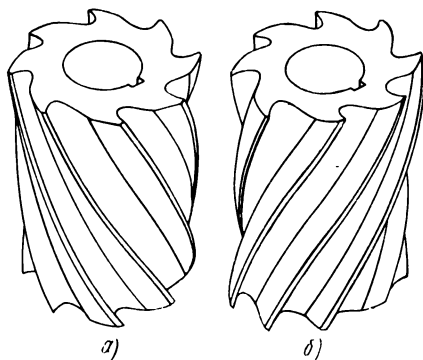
Цилиндрические фрезы с винтовыми зубьями
